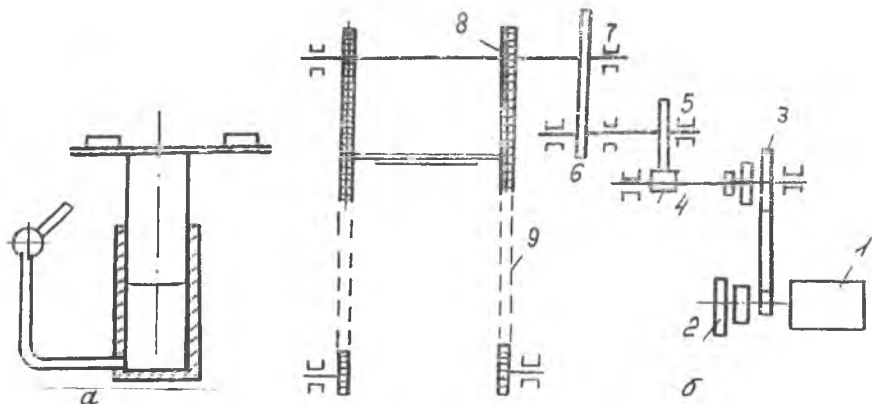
Схема литейных машин с опускающимся столом: а — гидравлический привод, б — механический привод, 1 — двигатель, 2, 3 — шкивы ременной передачи; 4, 5 — червячная пара; 6, 7 — цилиндрические шестерни; 8 — звездочки, 9 — цепи Галля
